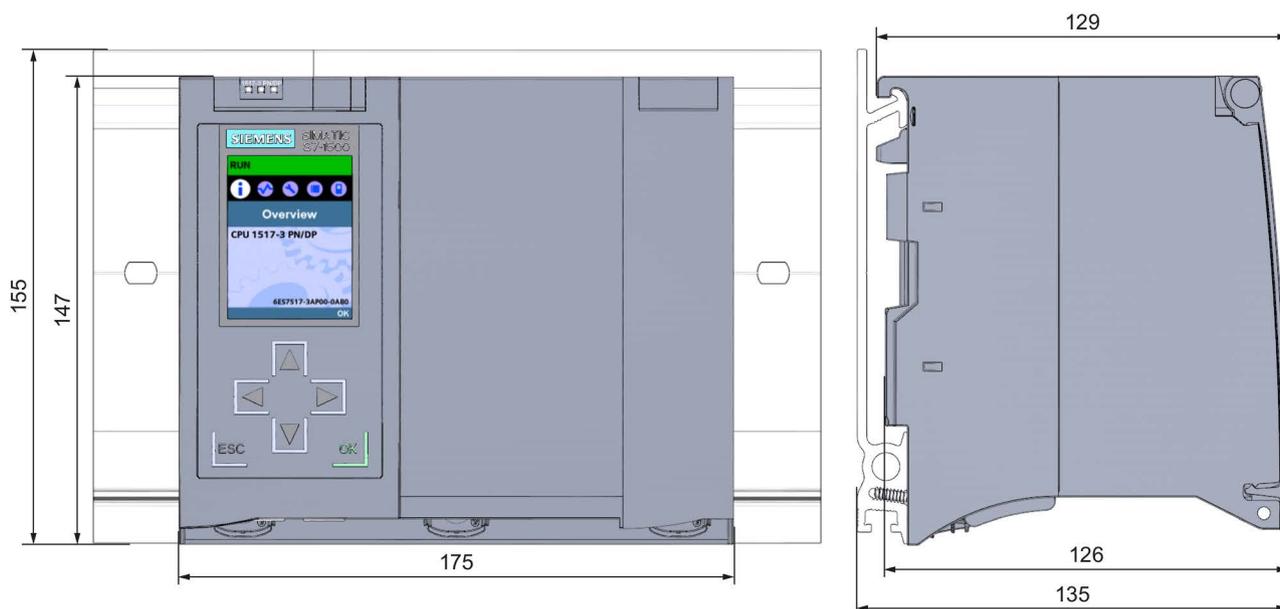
Maßbild der CPU 1517-3 PN/DP, Front- und Seitenansicht
